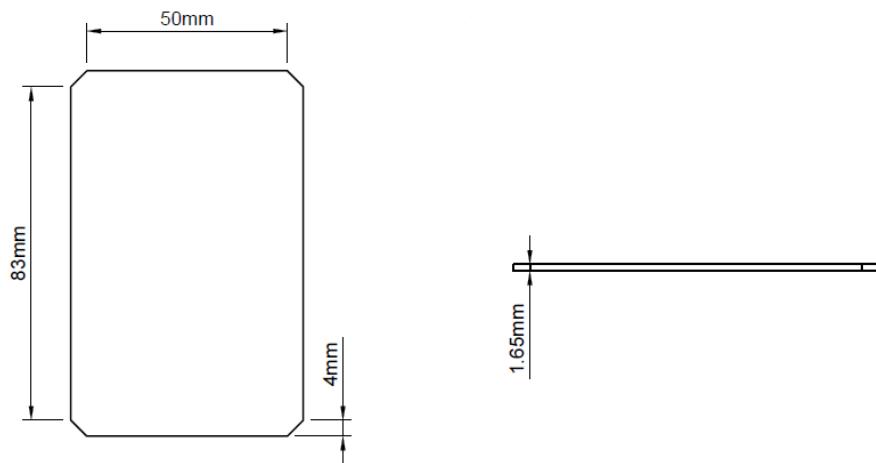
Dibujo y dimensiones de la placa o circuito impreso
